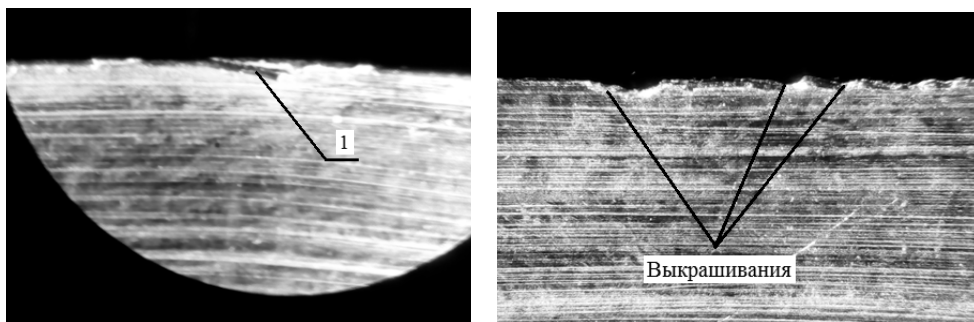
Режущая поверхность дискового ножа. ×50
